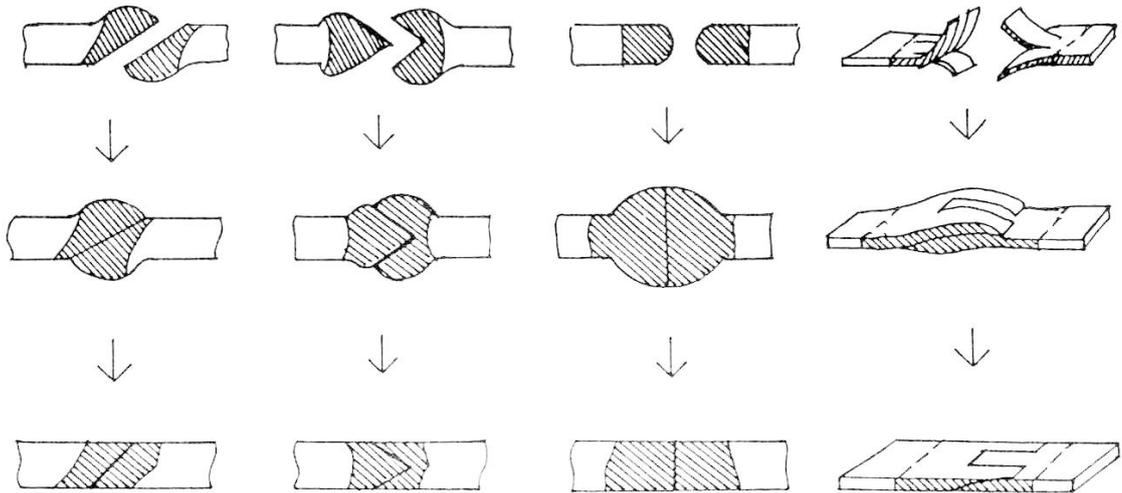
Приклади ковальських з'єднань та обробки деталей огорож
